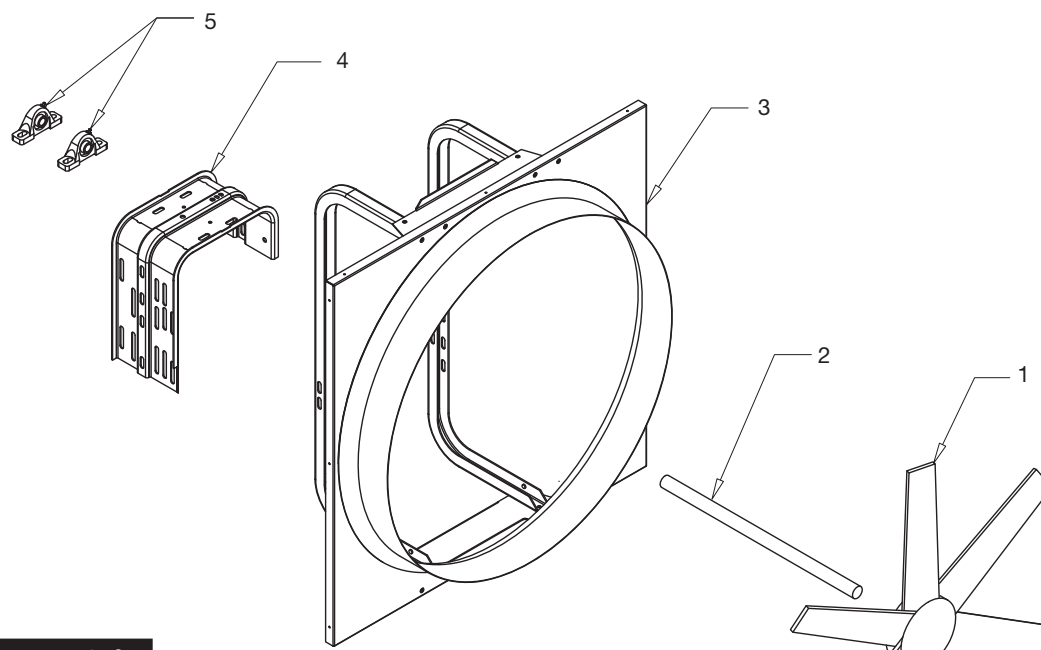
Pièces de rechange pour ventilateurs d'extraction/soufflage réversibles à courroie
